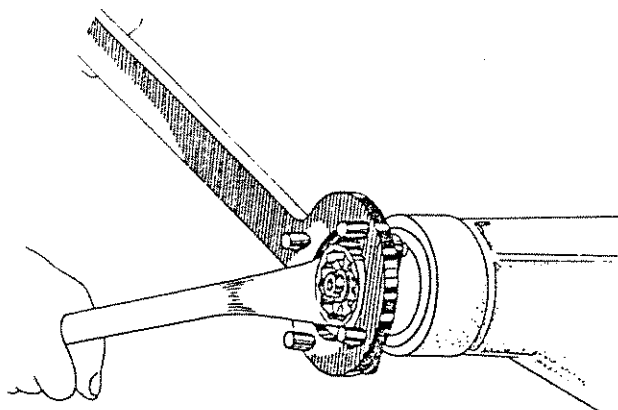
Anwendung des Spezialwerkzeuges 20SM.90 zum Ausbau des Antriebsflansches
